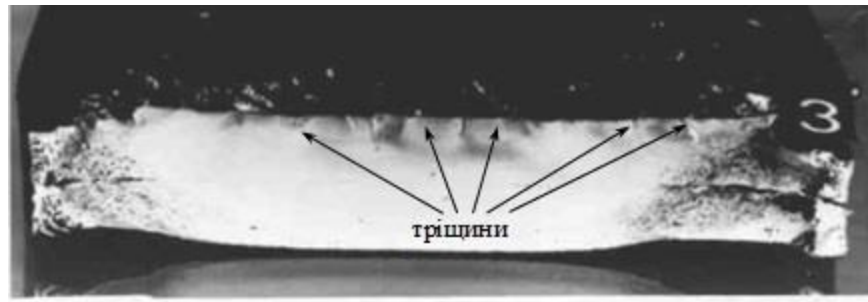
Поверхня втомного руйнування зразка в зоні зварного шва, що демонструє багатоосередковий характер зародження поверхневих тріщин та їх об'єднання
